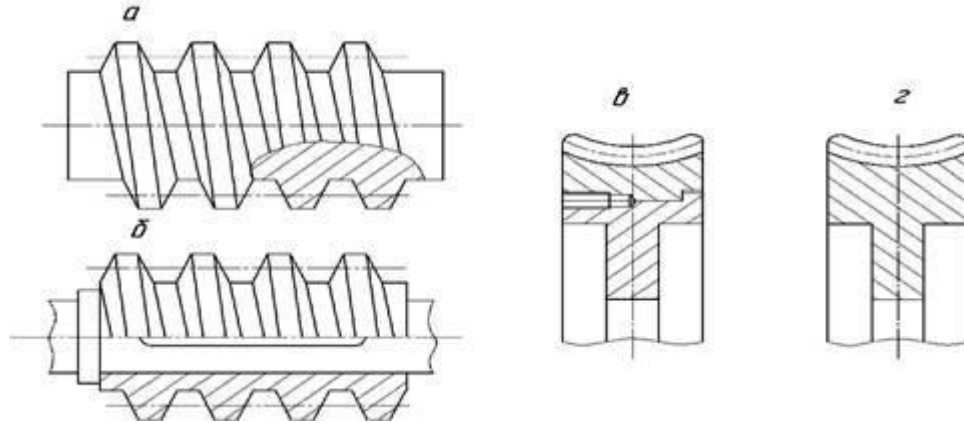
Конструктивні схеми черв'яка і черв'ячного колеса
